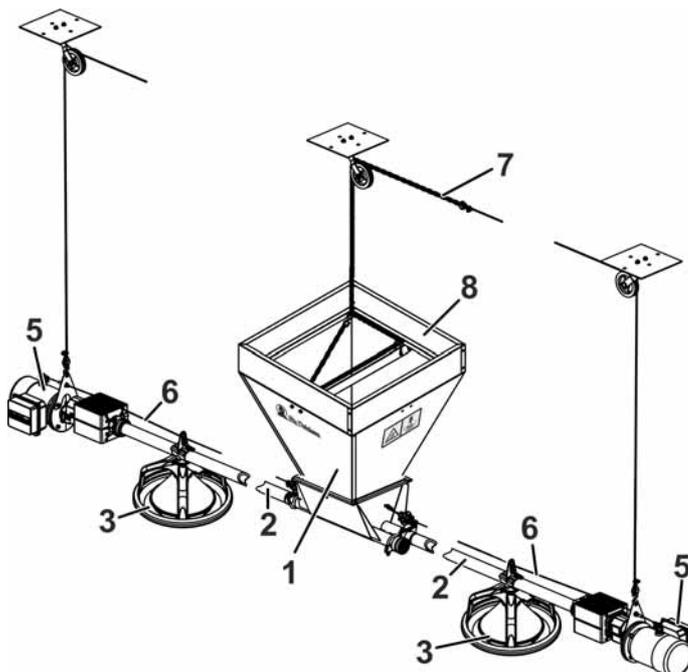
Futterlinie mit Futterbehälter 2-Linien mittig
